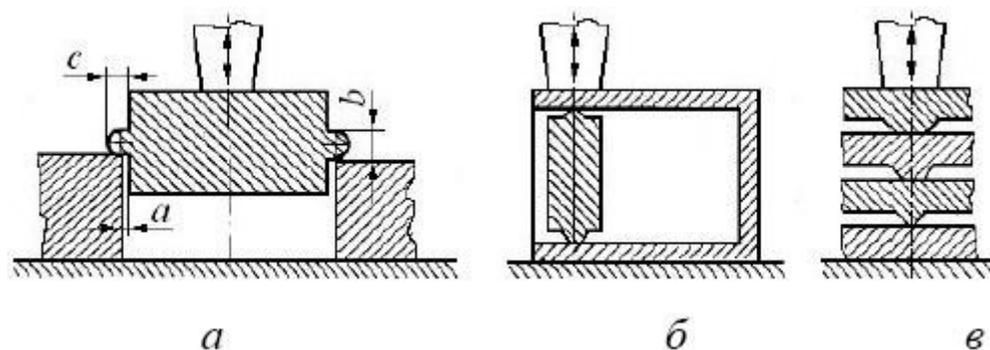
Технологическая подготовка кромок в случаях ультразвукового прессования (а), сварки в двух плоскостях (б), многоэлементной сварки (в); $a = 0,01-0,25$ мм; $b = 0,25-1,25$ мм; $c = 0,25-1,25$ мм
